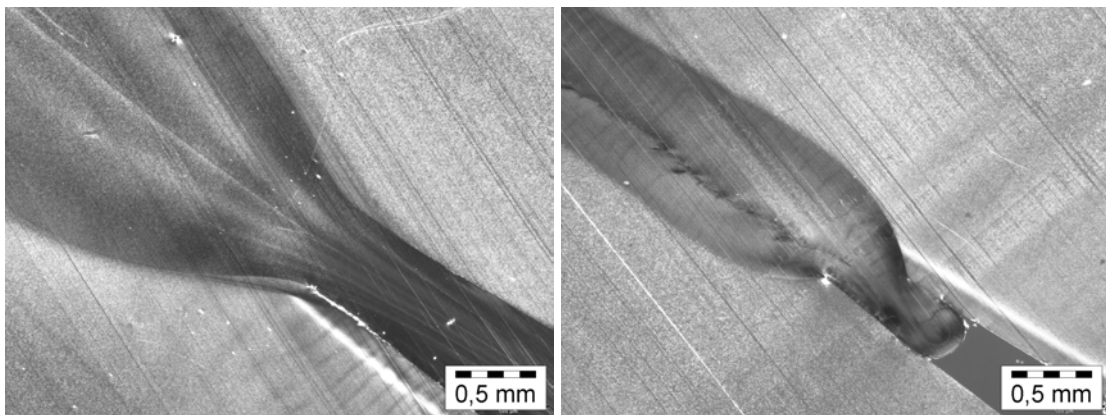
Über einen Zeitraum von 720 Stunden mit dem realen Sickerwasser der Deponie Braunschweig-Watenbüttel beaufschlagte Überlappschweißnähte der Schweißnahtserien S2 (links) und S7 (rechts) entnommene Dünnschnitte. Deutlich grenzt sich die Schmelze mit dem ausgetriebenen Schweißwulst vom so genannten Grundmaterial ab. Darüber hinaus ist die unterschiedliche geometrische Ausbildung der Schweißnaht zu erkennen. Polarisationsoptische Aufnahme.
